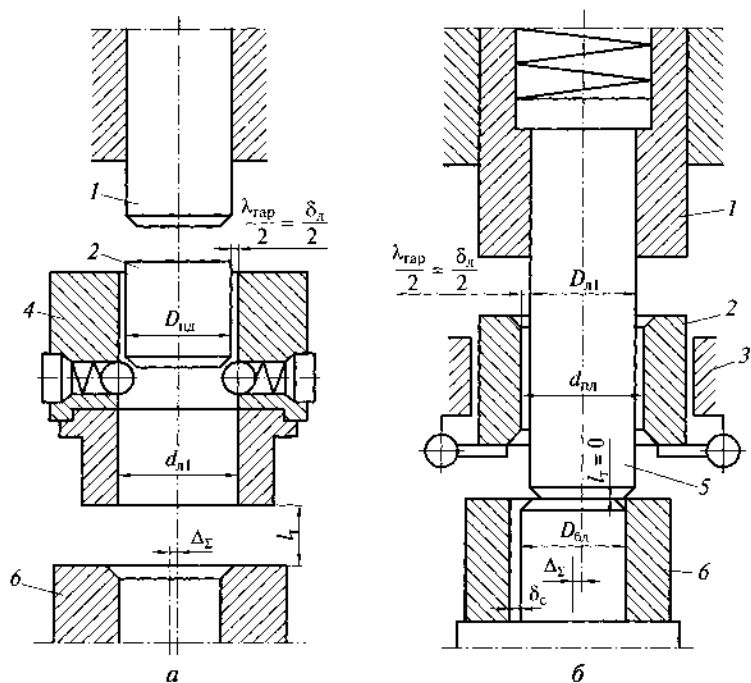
Схема простейших рабочих органов для автоматического соединения цилиндрических деталей с зазором:
